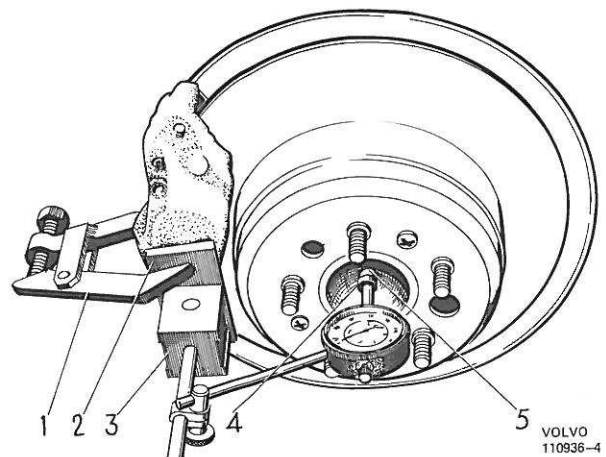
Mesure du jeu axial à l'arbre de roue motrice
